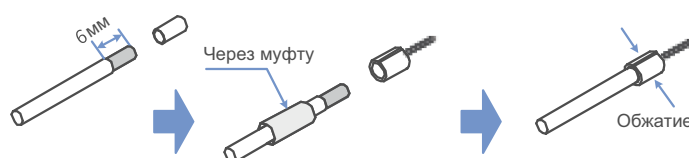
Подготовка кабеля со штырьковой клеммой
